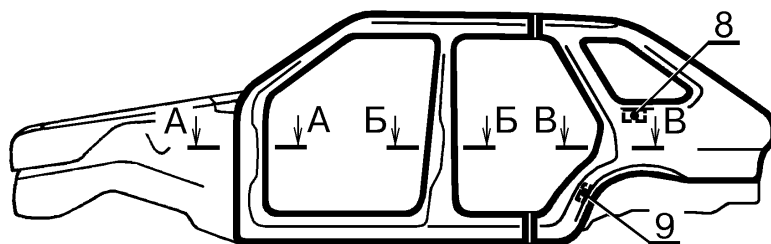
Детали боковины ВАЗ-2109; 21099; 2114; 2115 правой/левой: установка и приварка усилителей на панели боковины. Номера и наименования деталей, количество сварочных точек приведены в таблице 7.
